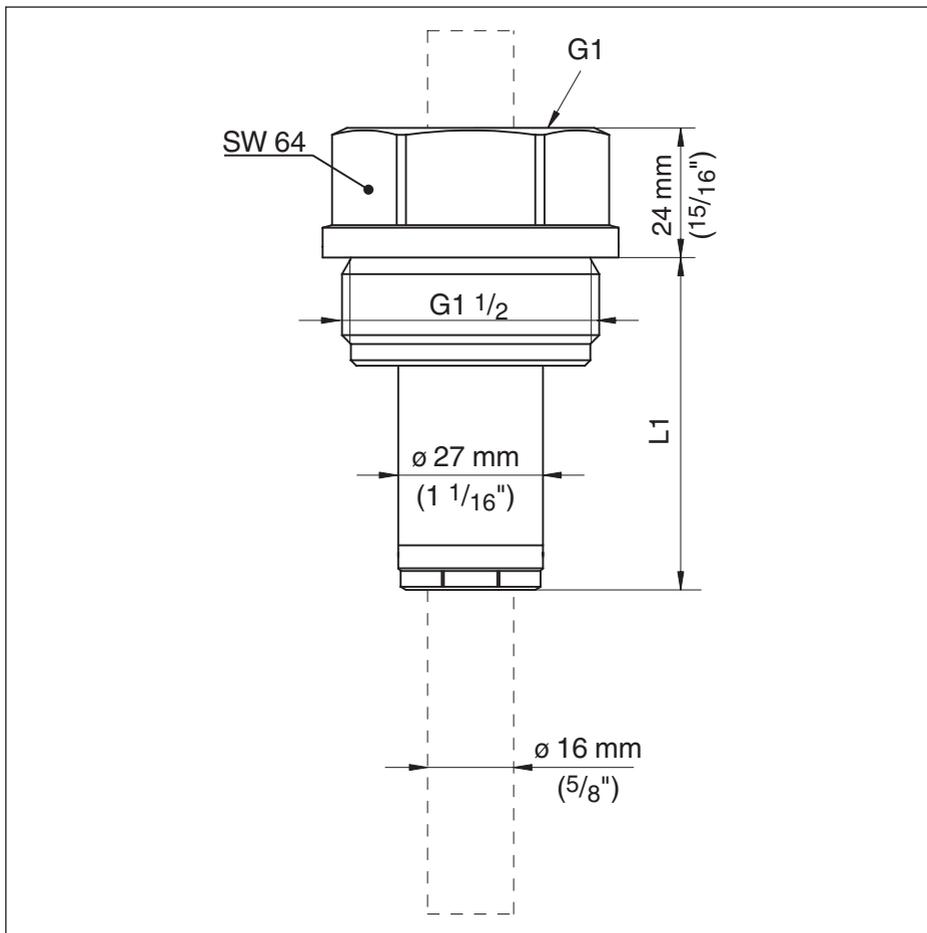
Adaptador com tubo de blindagem, vedado por vácuo para VEGACAL/VEGACAP, haste \varnothing 16 mm (0.63 in)
